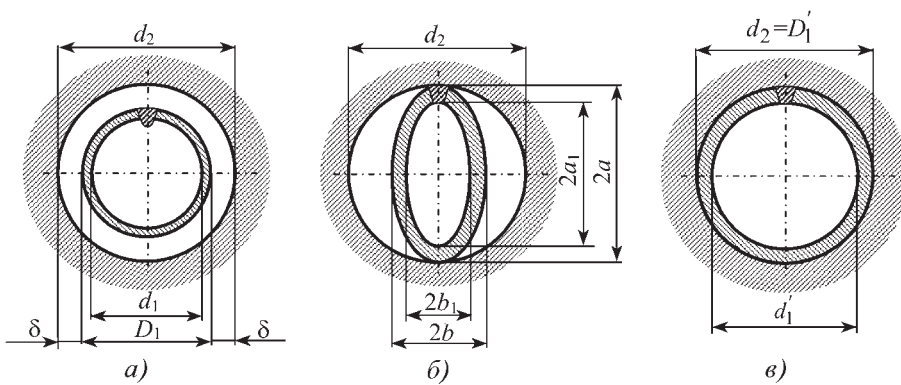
Этапы деформации поперечного сечения сварной трубы, установленной в охватывающий цилиндр с зазором $2\delta > 2\delta_{\min}$:
